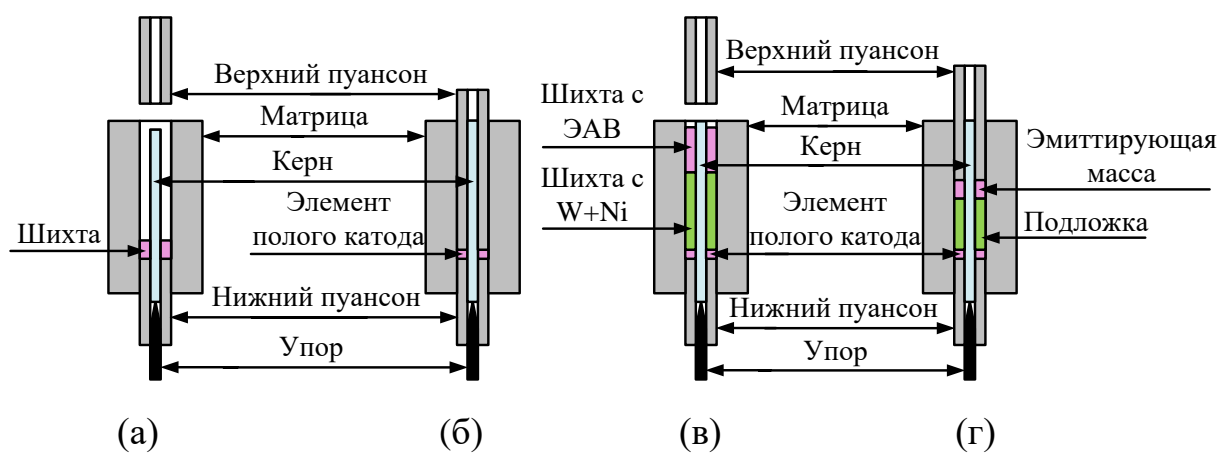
Процессы прессования заготовок электродов: загрузка шихты для прессования элемента полого катода (а) , прессований элемента полого катода (б), пресс-форма с загруженной шихтой материала подложки и материала с активно-эмиссионным веществом (в) и спрессованная заготовка электрода в пресс-форме (г)
